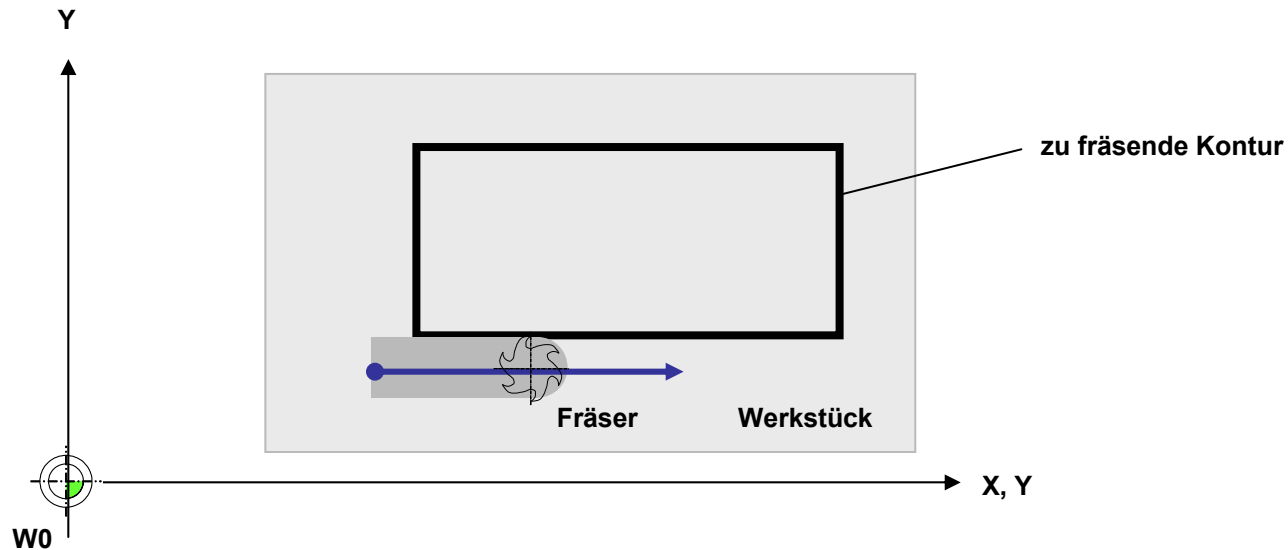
Beispiel für eingeschaltete Fräserradiuskorrektur
